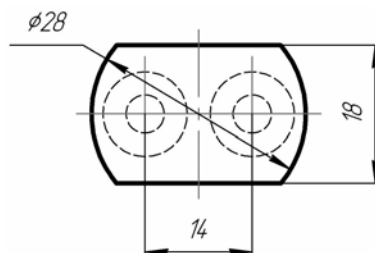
Схема поперечного сечения заготовки и вырезки образцов на растяжение
